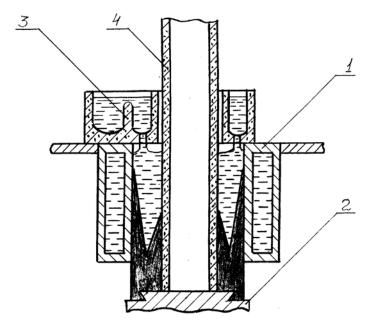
Схема процесса вертикального непрерывного литья.
